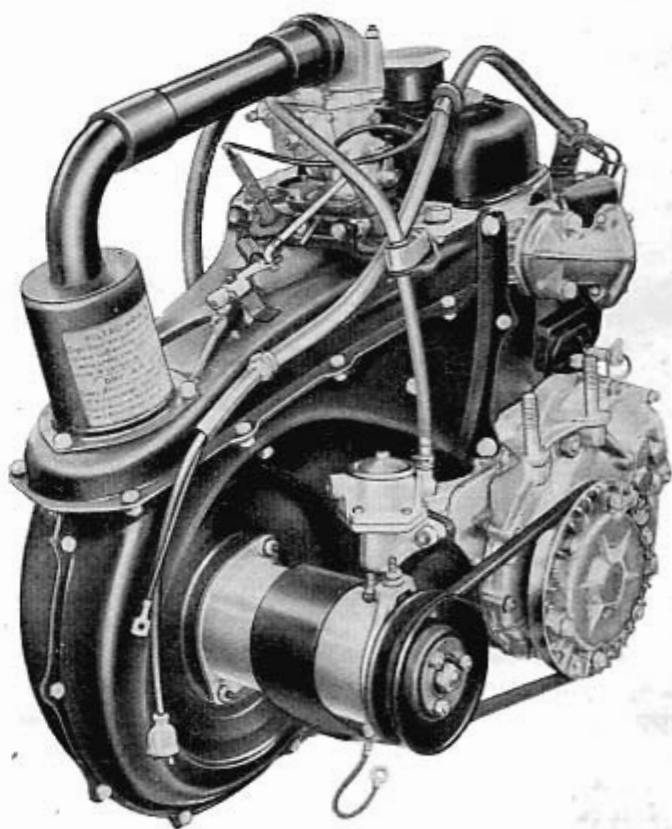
Ensemble moteur, vu du côté dynamo.
